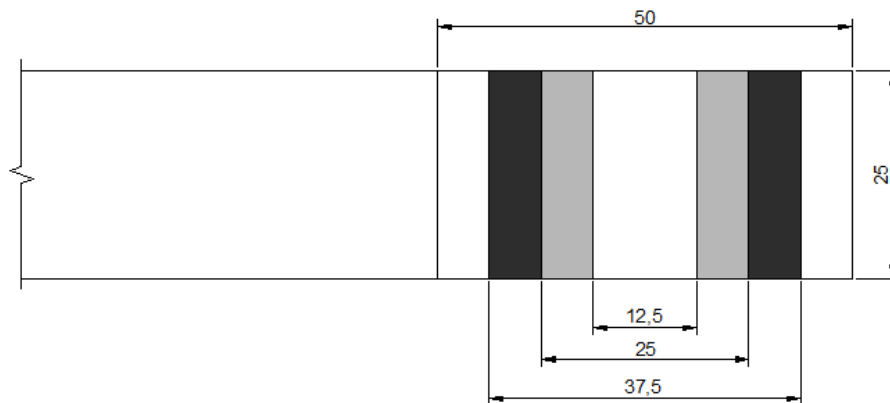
Localização e dimensões do defeito utilizado na junta de L_0 de 25 mm.
